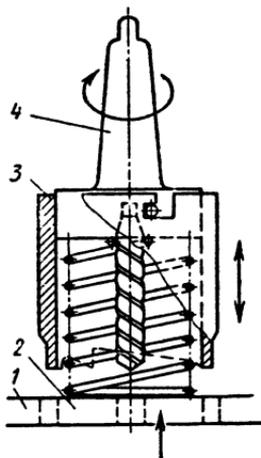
Обработка пластмассовых заготовок комбинированным сверлом с пружинным выталкивателем:
